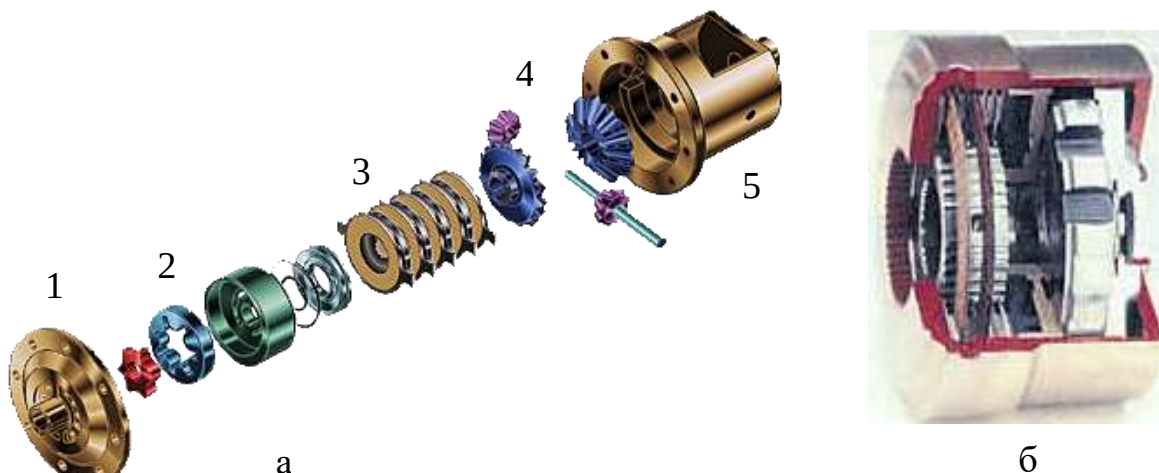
Геройдна муфта: а – устрій; б – загальний вигляд
